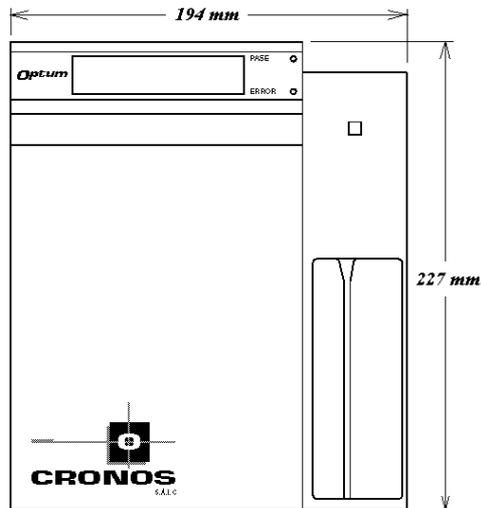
Dimensiones del Reloj Optum, Optum Tec
